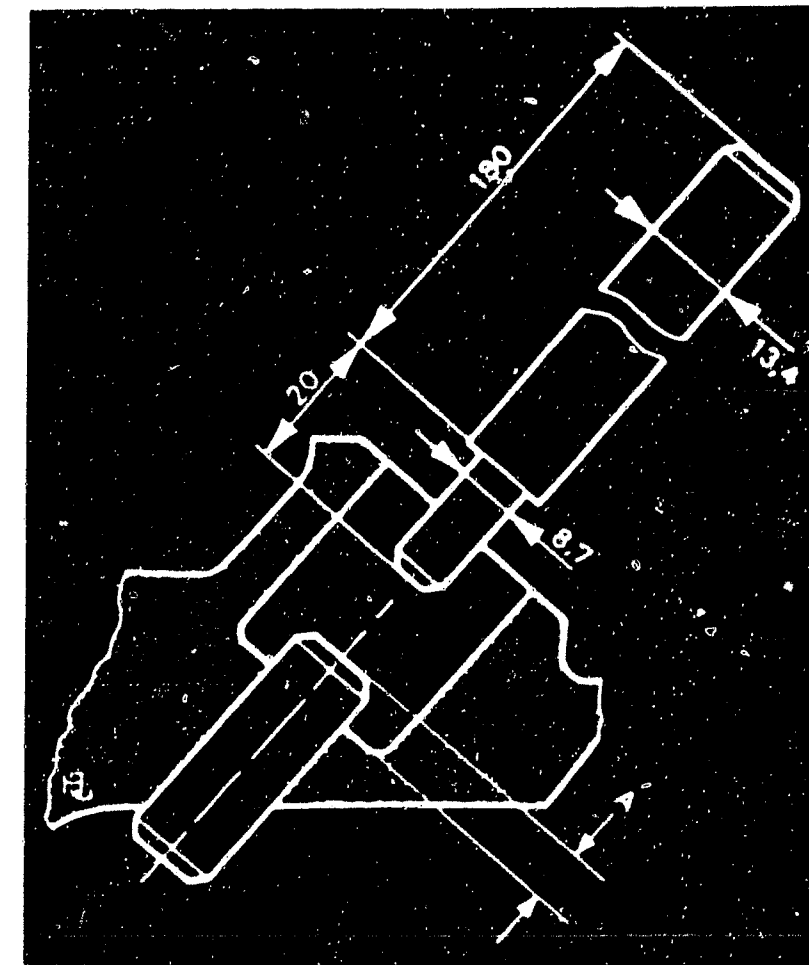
Die Ventilführungen lassen sich mit dem gezeigten Dorn (Masse in mm) aus- und eintreiben. Das Vorstehmass A beträgt am Einlassventil 13,3... 13,5mm, und am Auslassventil 16,3...16,5mm.
